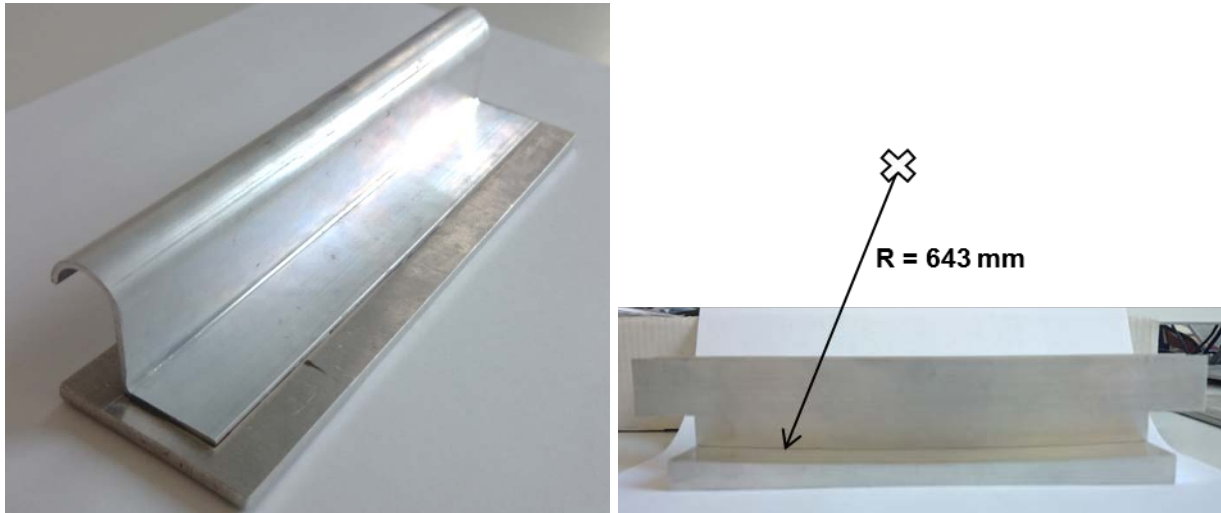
Links: Demonstrator Stringer auf Blech.
